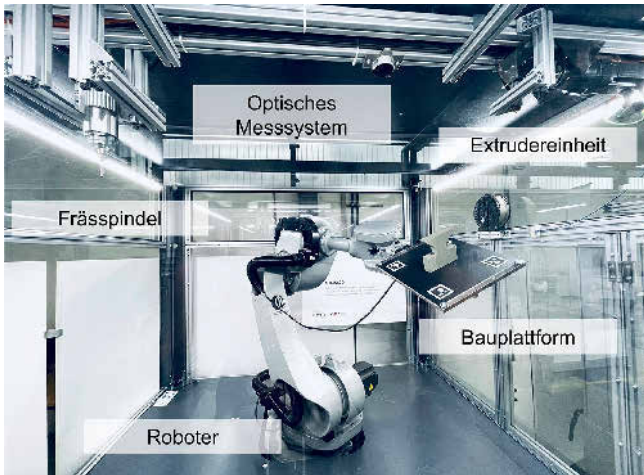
Demonstratoraufbau am Werkzeugmaschinenlabor WZL der RWTH Aachen University. Foto: WZL
